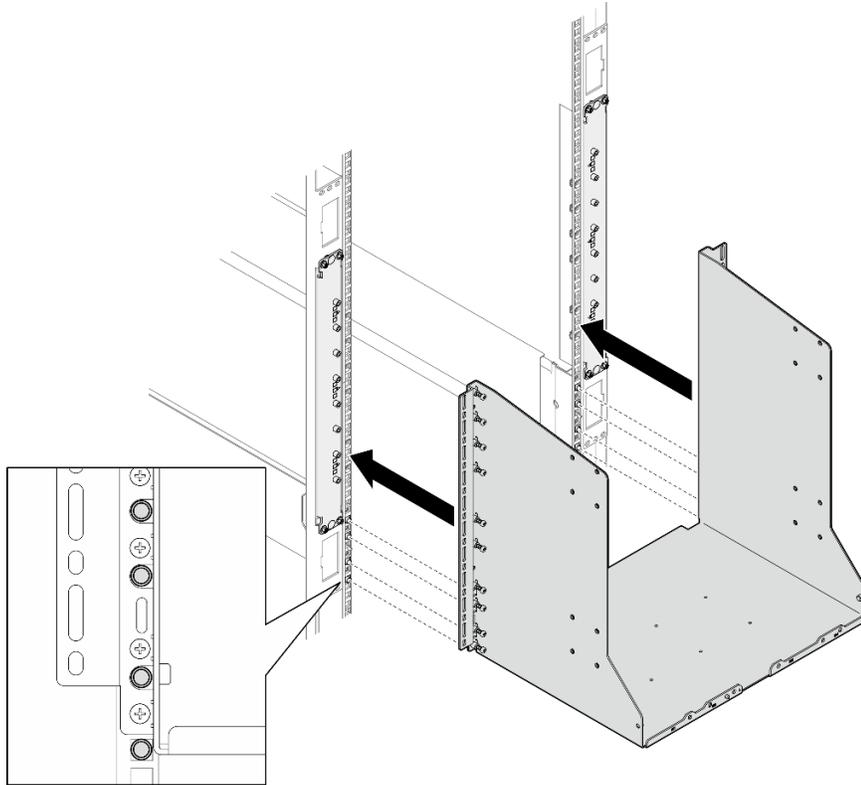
Alignement du support arrière sur les broches de guidage de la glissière
